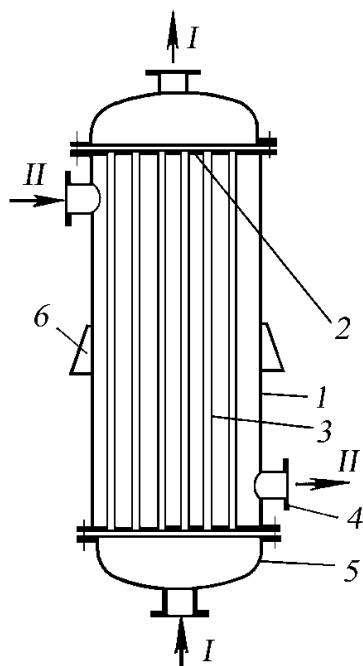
Вертикальний кожухотрубний теплообмінник з нерухомими трубними решітками: 1 – кожух; 2 – трубна решітка; 3 – труби; 4 – патрубок; 5 – кришка; 6 – опорна лапа; I, II – теплоносії
